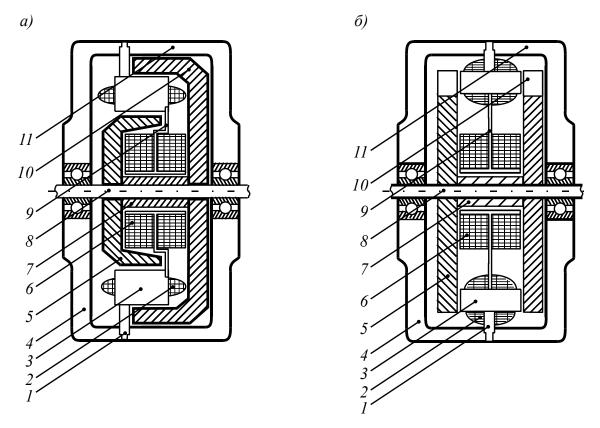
Индукторные генераторы: а — индукторный генератор с клювообразным ротором; б — индукторный генератор с зубчатым ротором: 1 — элемент крепления обмотки статора; 2 — обмотка статора; 3 — сердечник обмотки статора; 4 — передняя крышка; 5 — передняя полюсная половина; 6 — обмотка возбуждения; 7 — втулка; 8 — вал; 9 — элемент крепления обмотки возбуждения; 10 — задняя полюсная половина; 11 — задняя крышка
